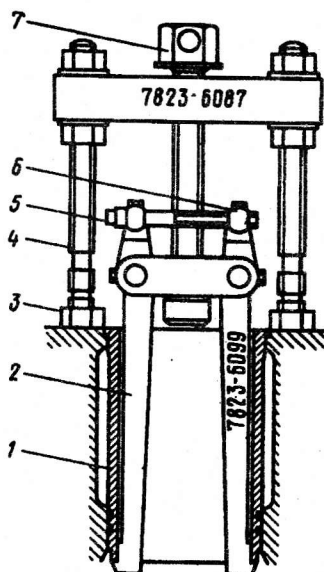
Выпрессовка гильзы из блока цилиндров комбинированным съемником:
